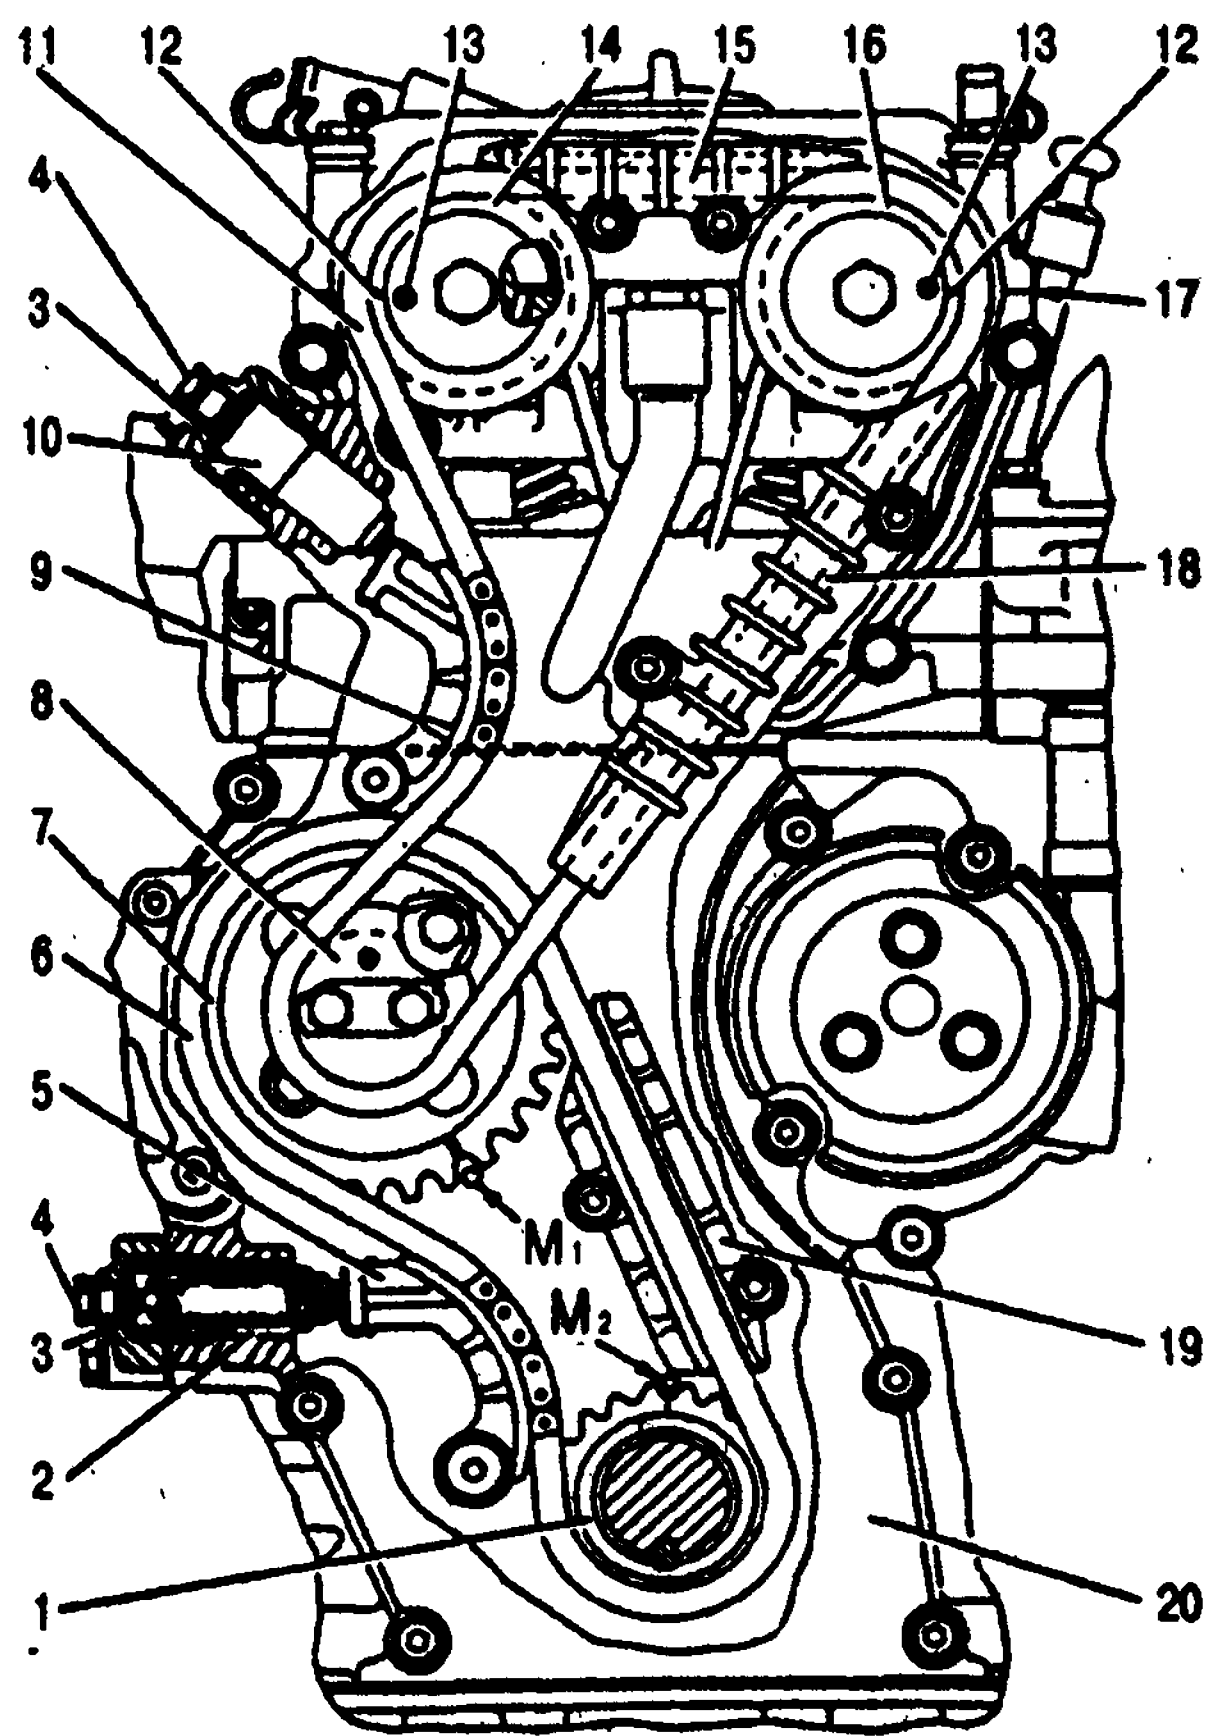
Привод распределительных валов: 1 - звездочка коленчатого вала; 2 - гидронатяжитель нижней цепи; 3 - шумоизолирующая резиновая шайба; 4 - пробка; 5 - башмак гидронатяжителя нижней цепи; 6 - нижняя цепь; 7 - ведомая звездочка промежуточного вала; 8 - ведущая звездочка промежуточного вала; 9 - башмак гидронатяжителя верхней цепи; 10 - гидронатяжитель верхней цепи; 11 - верхняя цепь; 12 - установочная метка на звездочке; 13 - установочный штифт; 14 - звездочка распределительного вала впускных клапанов; 15 - верхний успокоитель цепи; 16 - звездочка распределительного вала выпускных клапанов; 17 - верхняя плоскость головки блока цилиндров; 18 - средний успокоитель цепи; 19 - нижний успокоитель цепи; 20 - крышка цепи; M1 и M2 - установочные метки на блоке цилиндров
